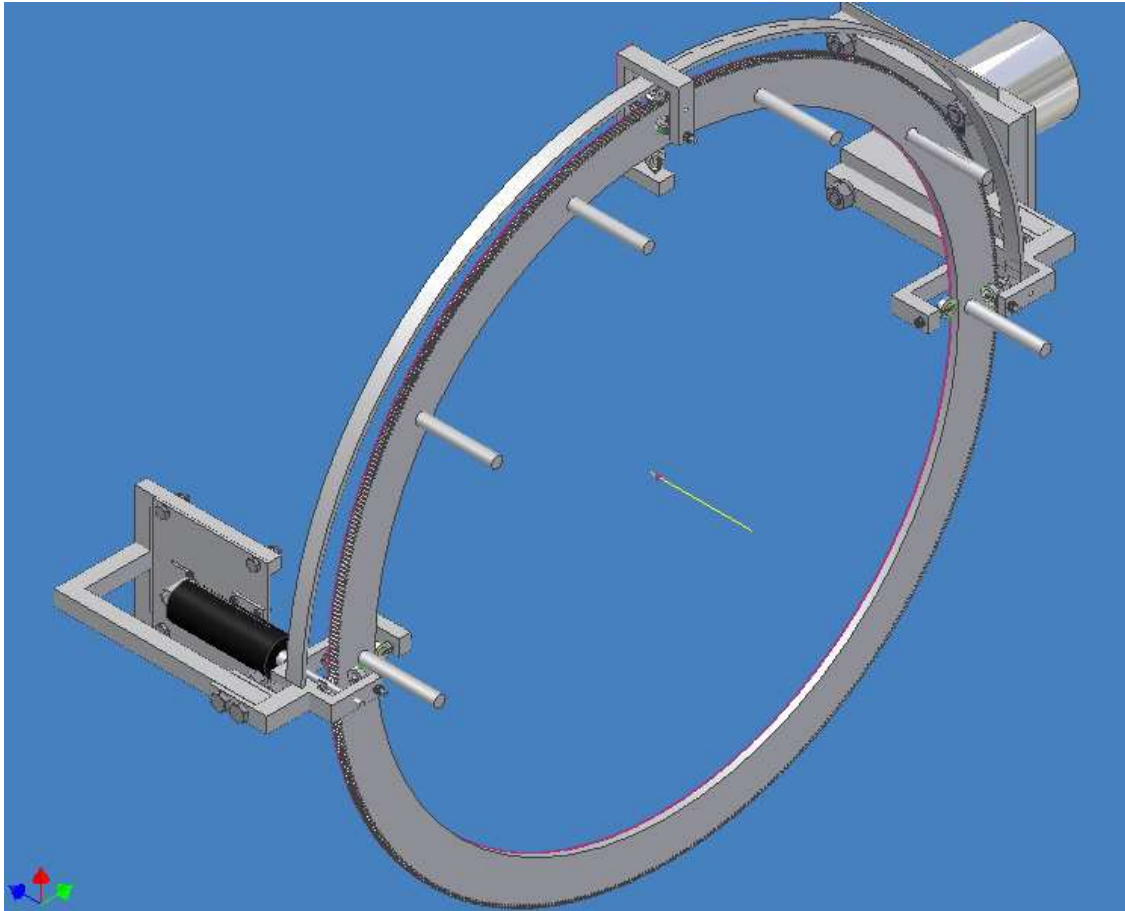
Vista isométrica superior derecha del equipo mecánico-nucleónico
